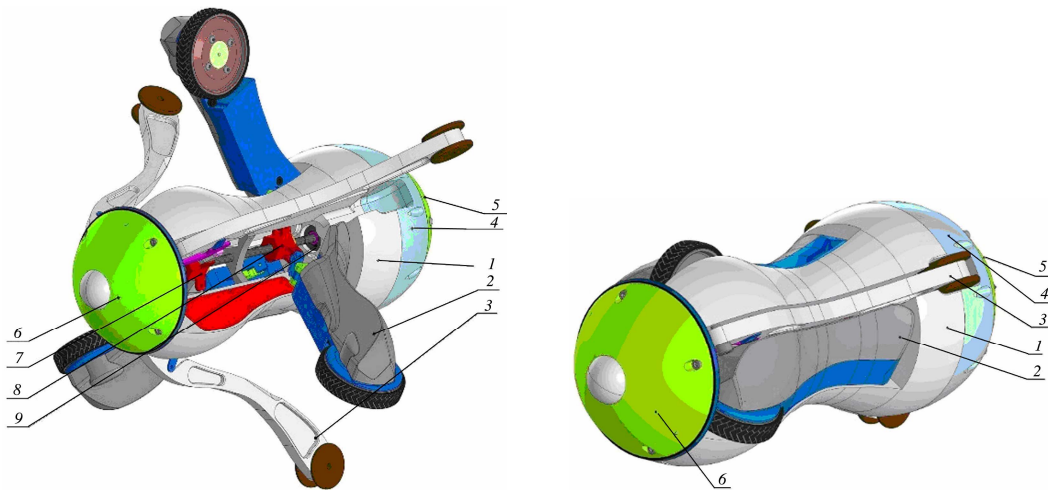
Предлагаемая конструкция ВРК: 1 – корпус; 2 – нога приводная опорная с колесным движителем; 3 – нога неприводная опорная с колесным движителем; 4 – отсек корпуса; 5 – задняя крышка; 6 – передняя крышка; 7, 8 – механическая система рычагов неприводных и приводных опорных ног; 9 – ось
